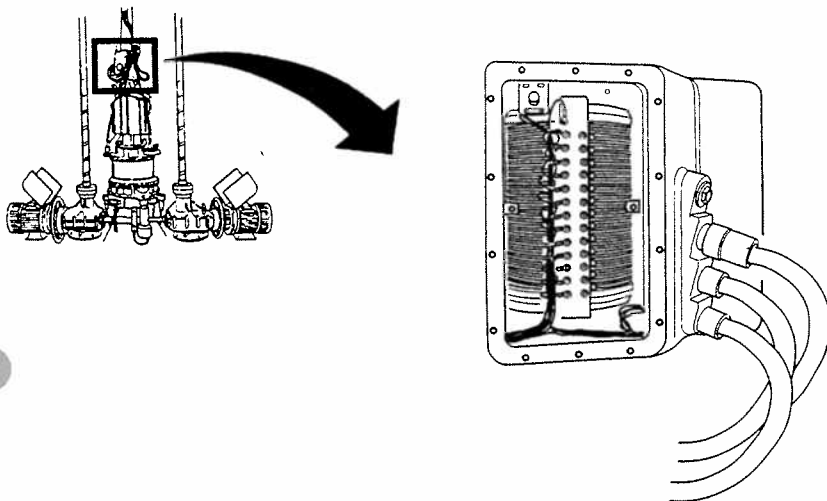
Släpringsenhet med insprutningsluckan bortmonterad
